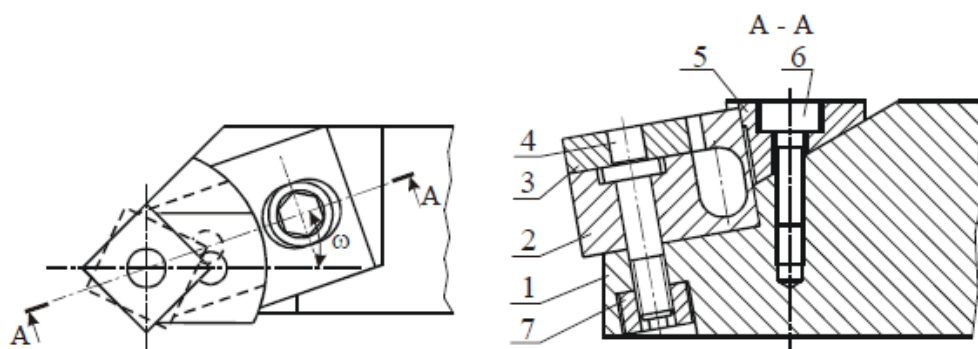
Універсально-збірний різець із поворотною робочою частиною: 1 - державка, 2 - поворотна підкладка, 3 - багатогранна непереточувана пластина, 4 - штифт, 5 - затискний елемент, 6 - гвинт, 7 – гайка. [10]
